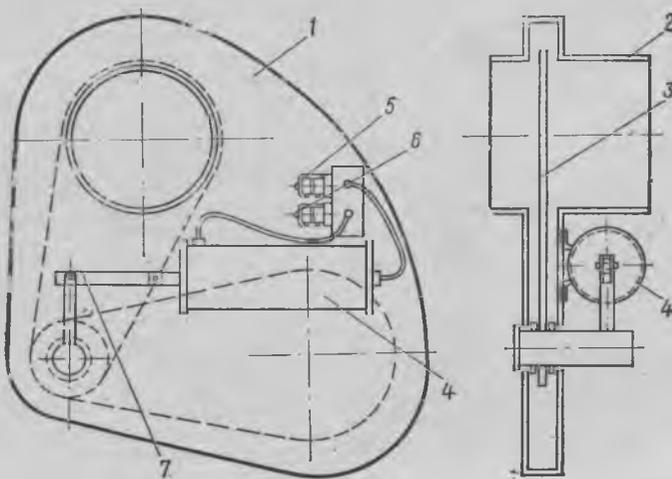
Воздушная заслонка: 1 — корпус; 2 — трубопровод; 3 — заслонка; 4 — воздушный цилиндр; 5, 6 — закрывающий и открывающий вентили; 7 — привод
